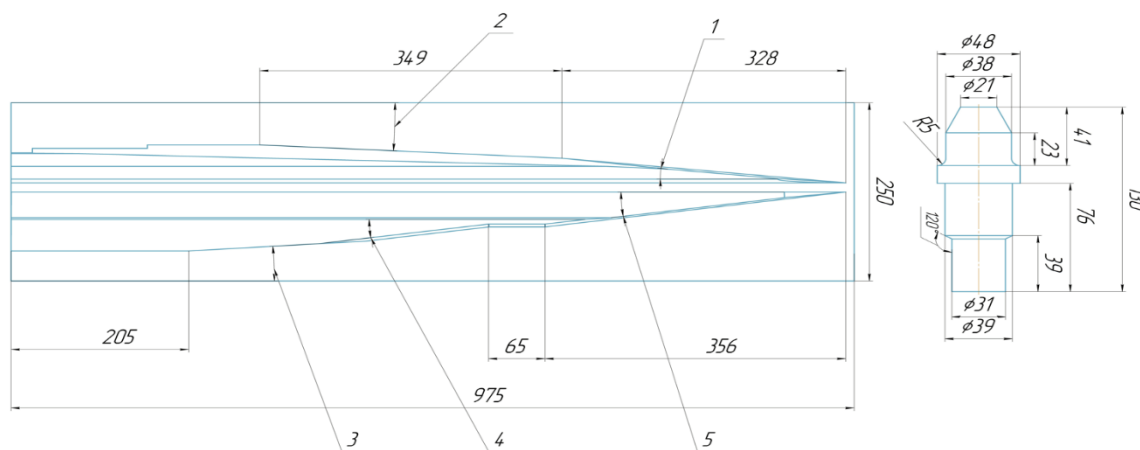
Клиновой инструмент (а) для ее изготовления зубок РКС1.00.00.111 (б) горнопроходческого комбайна
